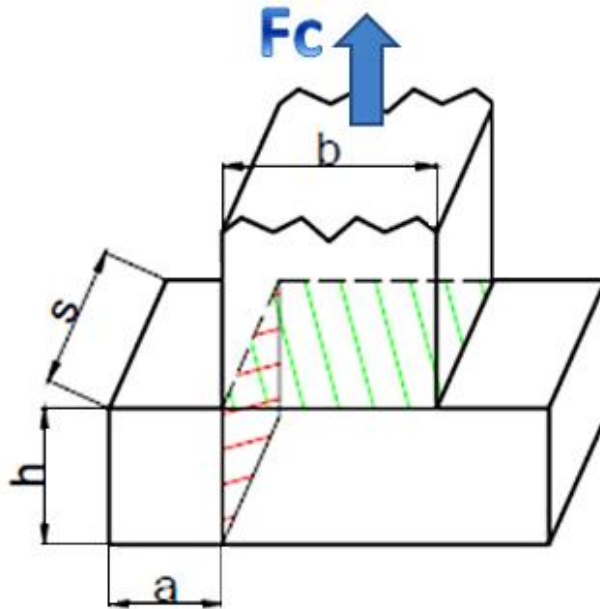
dimensioni principali del piede palare sottoposto alla forza centrifuga della parte superiore della pala.
